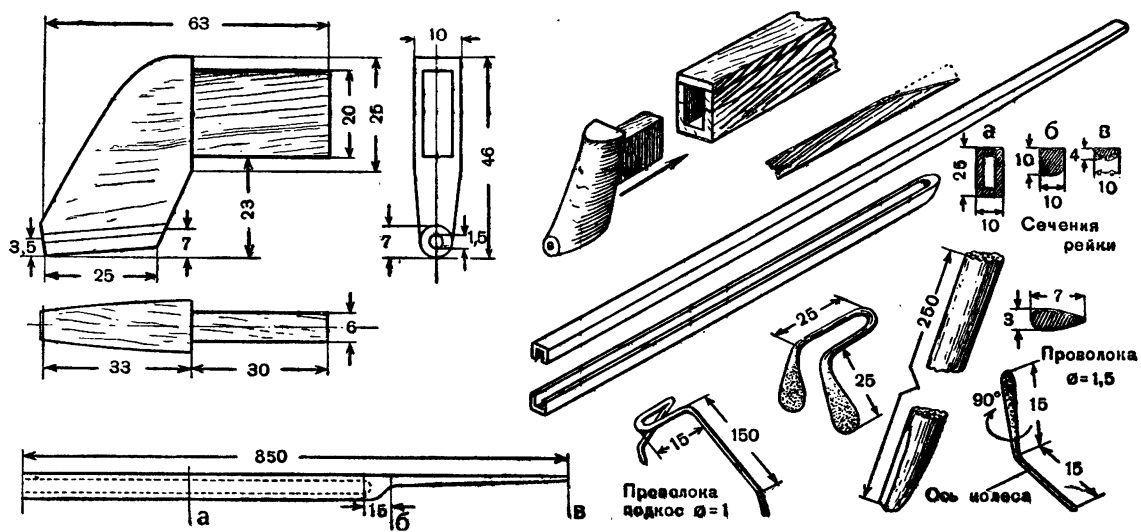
Конструкция рейки-фюзеляжа и подшипника схематической модели самолета парящего типа.
